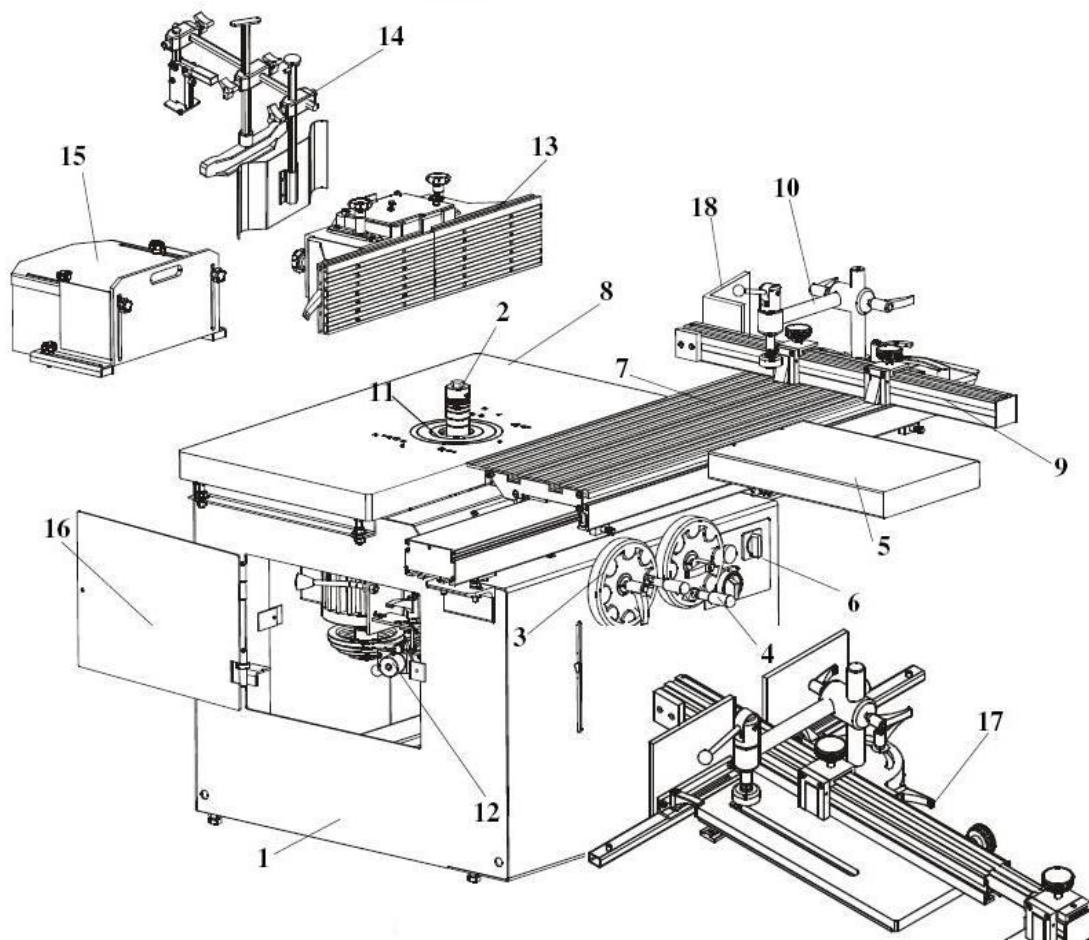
Конструктивное устройство фрезерного станка T1000L:
